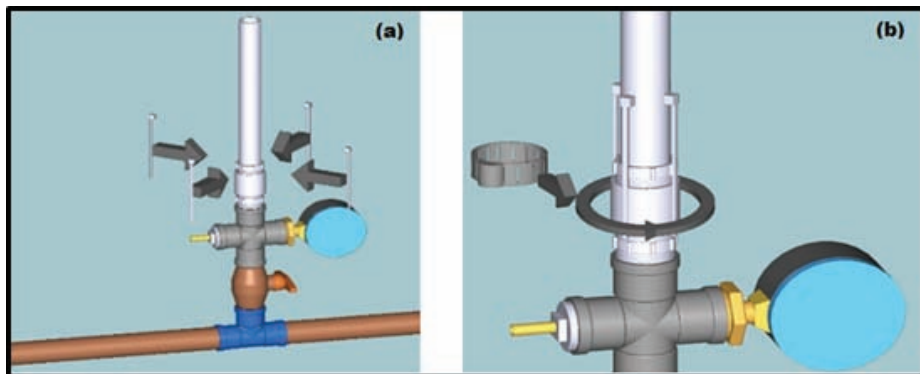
(a) Alocação das abraçadeiras plásticas na luva de PVC. (b) Fixação das abraçadeiras de plástico com a abraçadeira metálica com rosca sem fim.
